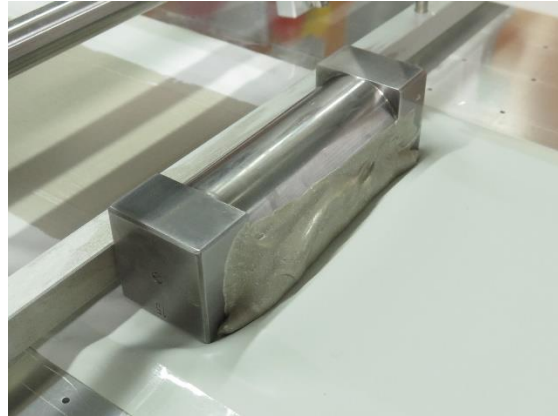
Aufbringen der leitfähigen Schicht mit einer Rakel
